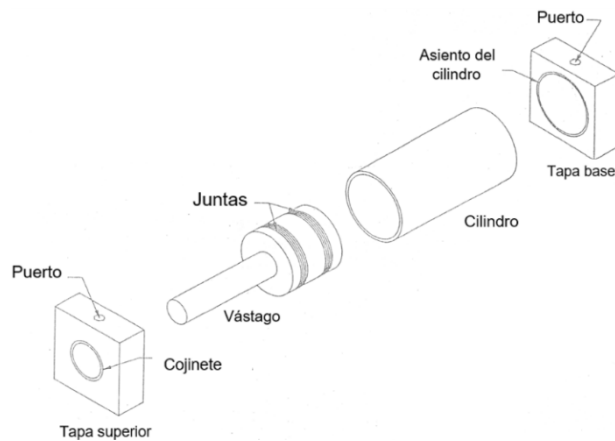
Partes principales conjunto cilindro-pistón^[6]
